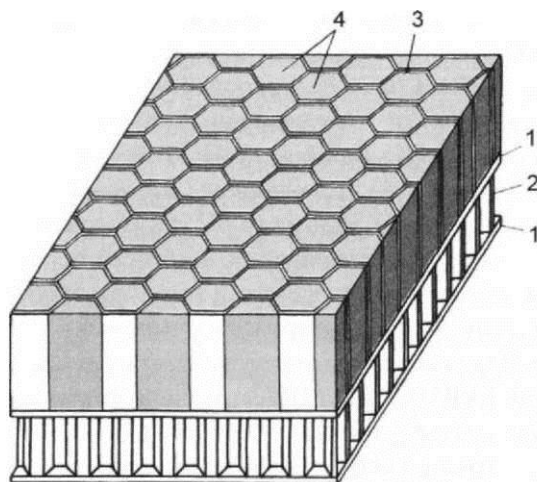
Схема фрагмента наружного контура командного отсека космического корабля АПОЛЛОН (США) I 1 - несущий слой; 2 - сотовый наполнитель; 3 - сотовый наполнитель из армированной пластмассы; 4 - эпоксидная смола с наполнителями
